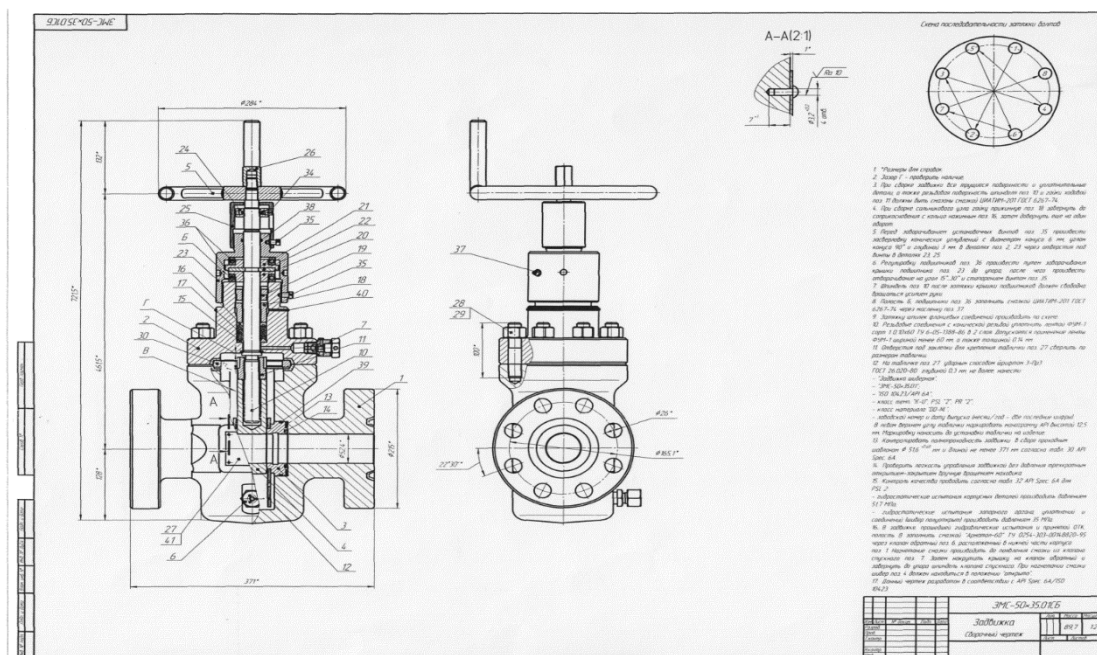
Сборочный чертеж задвижки ЗМС-50х35.01РР
